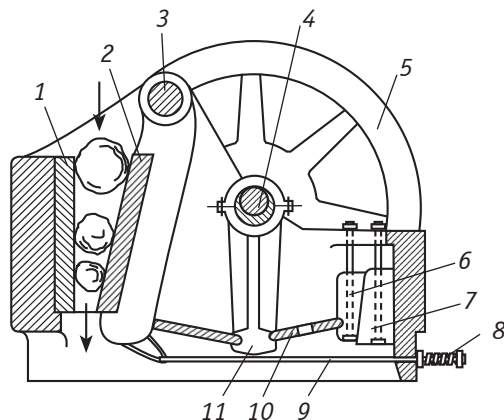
Схема щековой дробилки: 1, 2 — неподвижная и подвижная щёки; 3 — ось; 4 — вал; 5 — маховик; 6, 7 — распорные клинья; 8 — пружина; 9 — тяга; 10 — распорная плита; 11 — шатун
